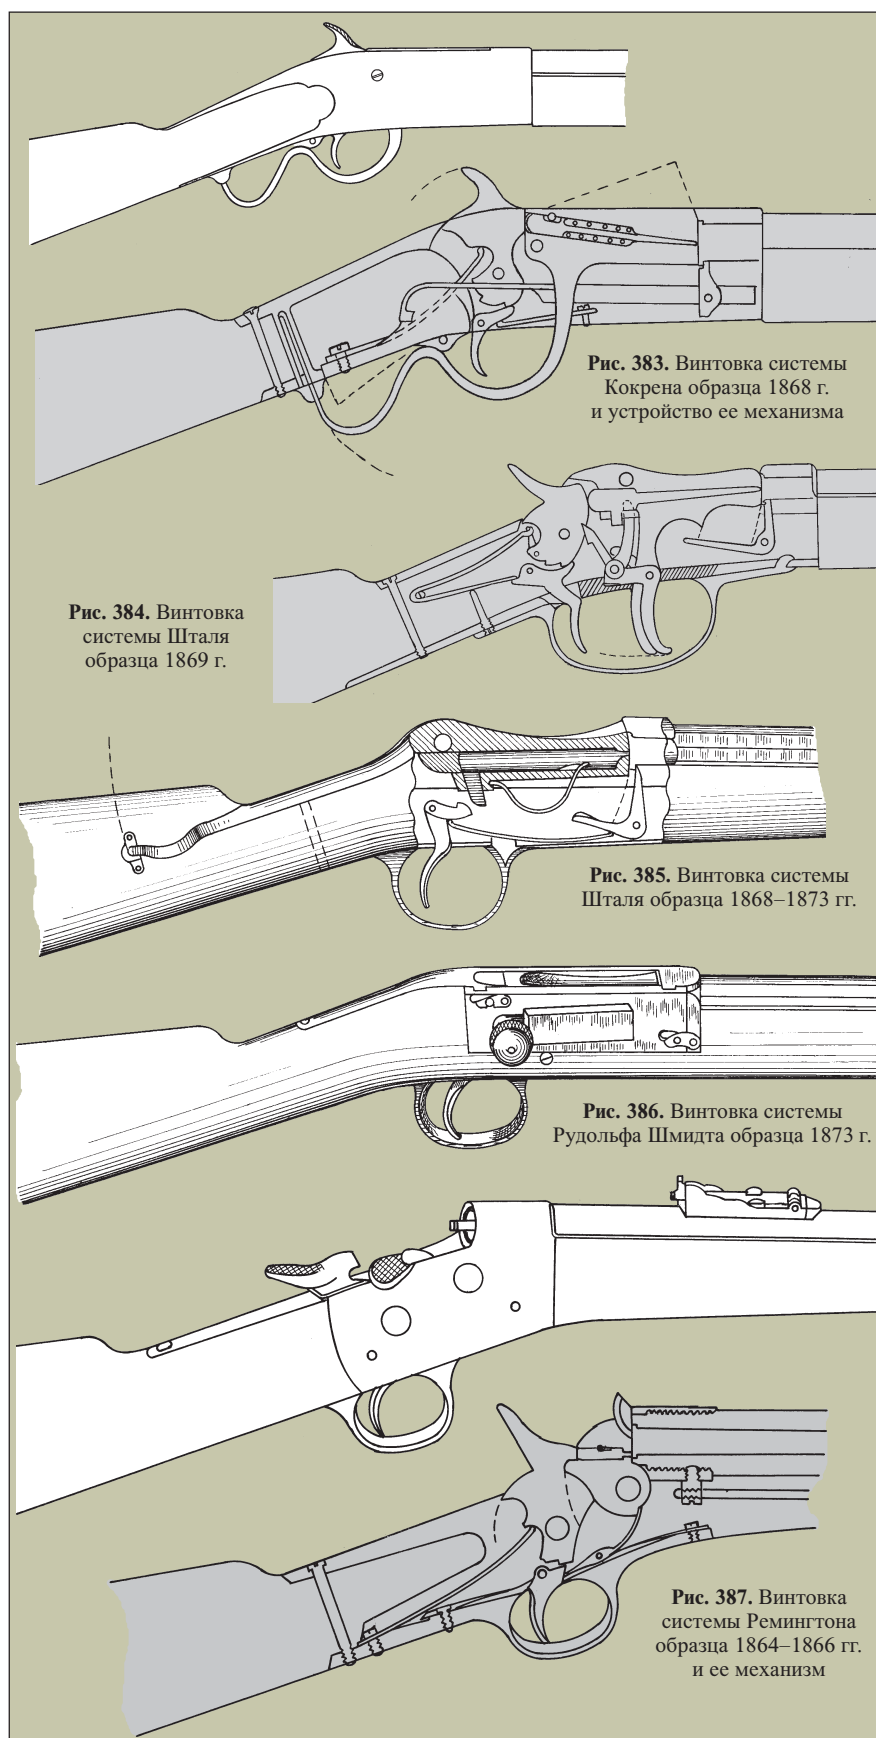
Винтовка системы Кокрена образца 1868 г. и устройство ее механизма
